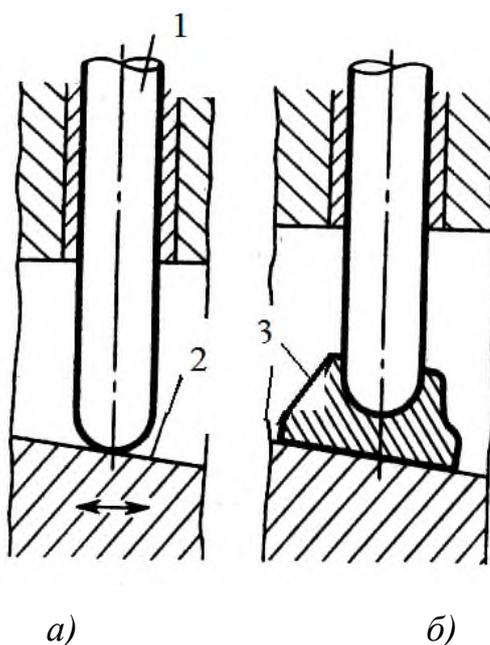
Замена линейного контакта толкателя 2 с наклонной шайбой 1 поверхностным контактом путем установки самоустанавливающейся пяты 3
